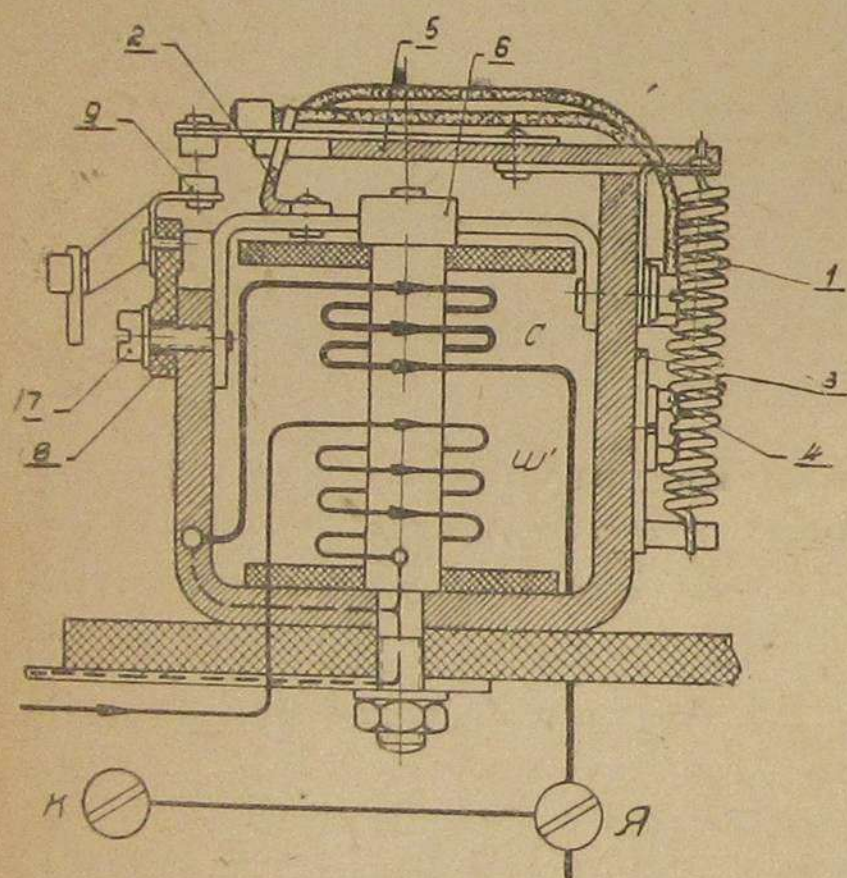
Конструктивная схема реле для автомобиля ЗИС.
